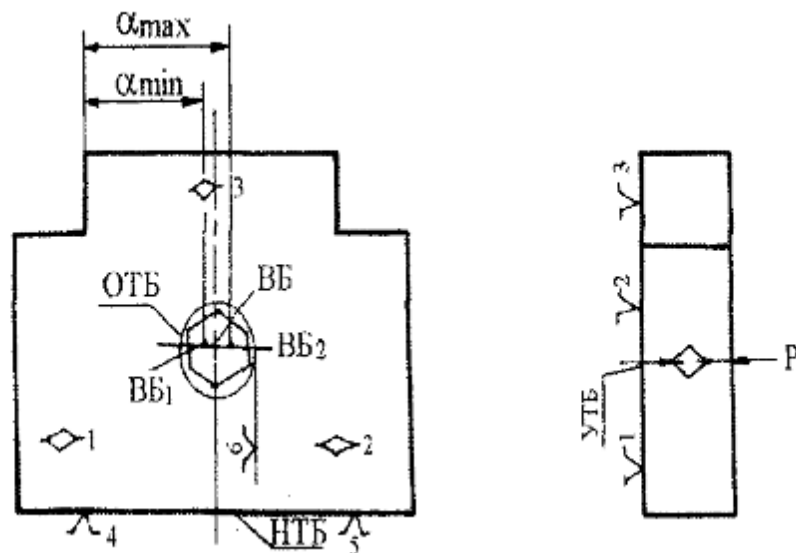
Теоретична схема базування деталі типу плита по двох площинах і отвору
